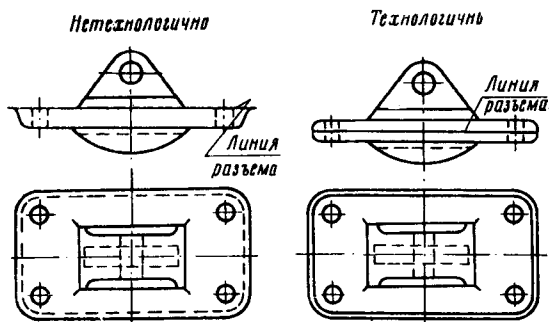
Линия разреза детали с двусторонними выступами.
